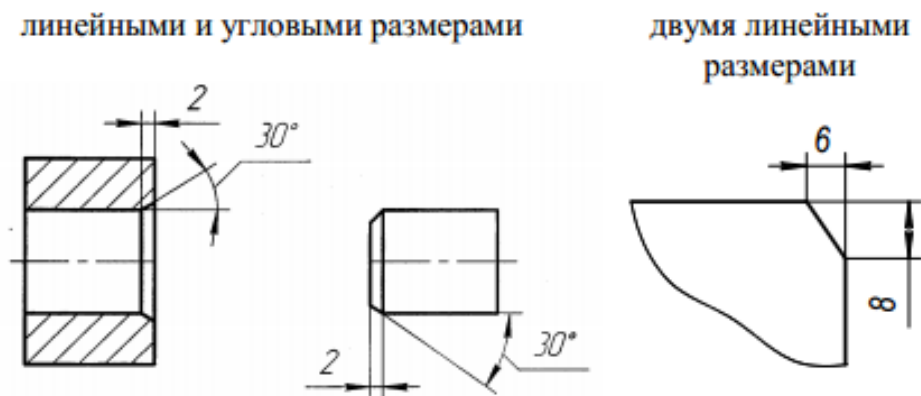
Способы нанесения размеров фасок под углами, отличными от 45°
